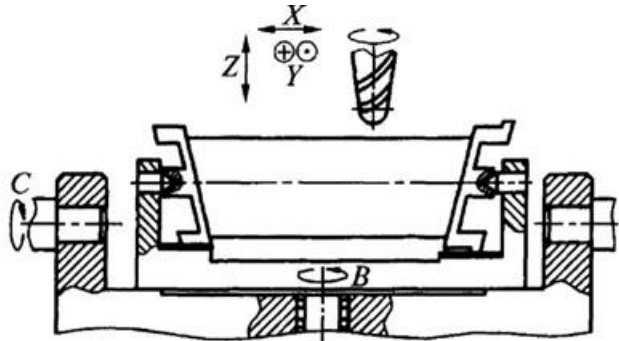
схема руху інструмента й заготовки при фрезеруванні профілю пера (варіант 1).
